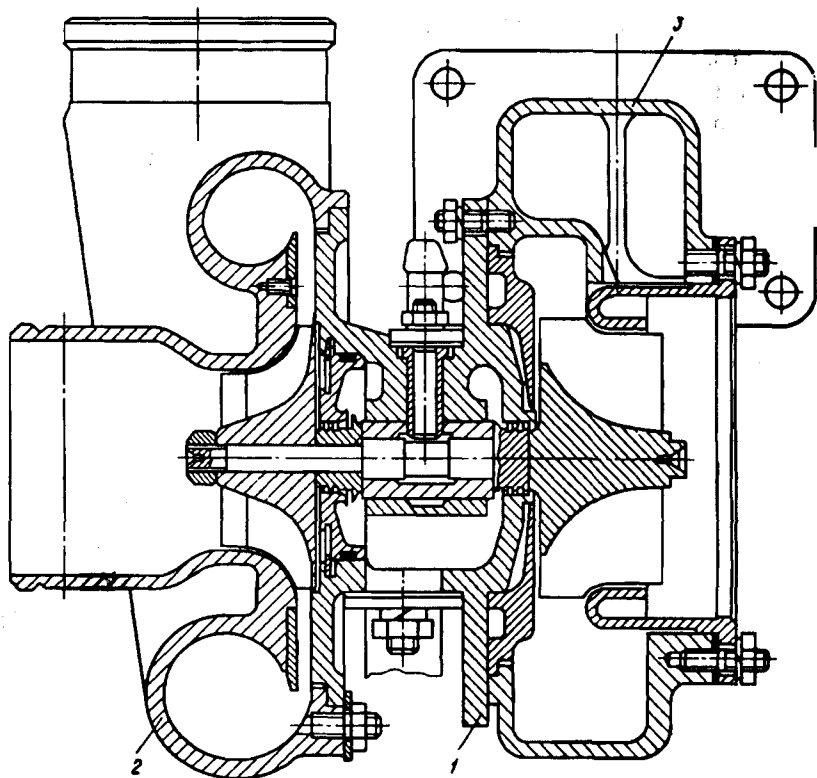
Турбокомпрессор типоразмера ТКР 9:
